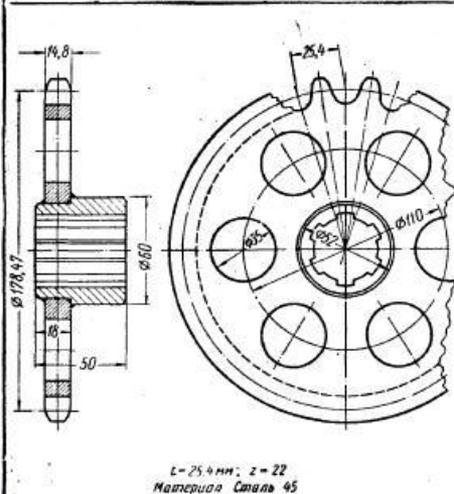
Звездочка для двухрядной втулочно-роликовой цепи
